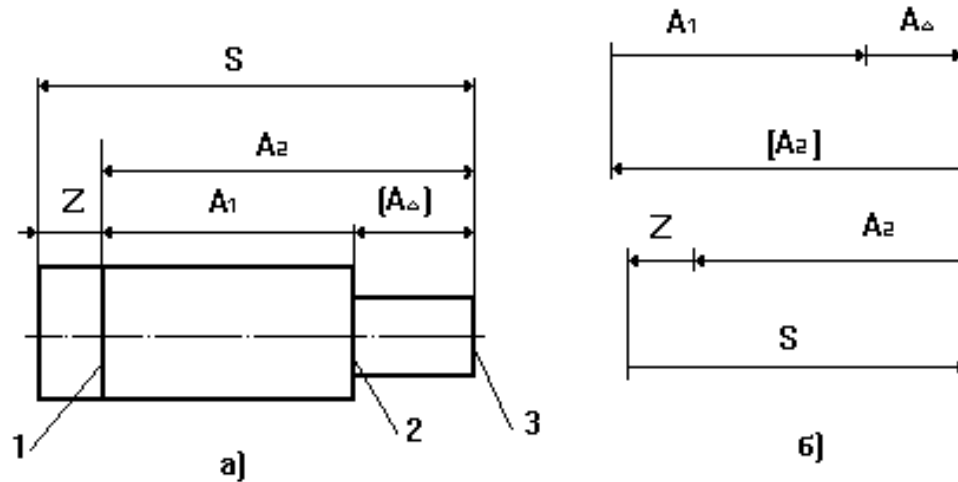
Схемы технологических размерных цепей при обработке вала на револьверном станке.
